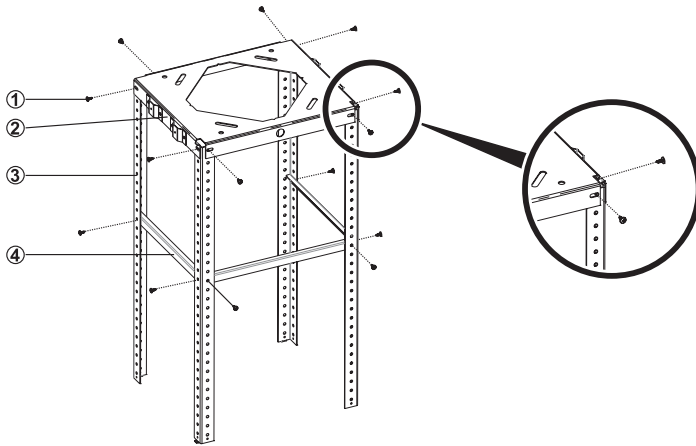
INSTALLAZIONE E COMPONENTI SEZIONE 2
